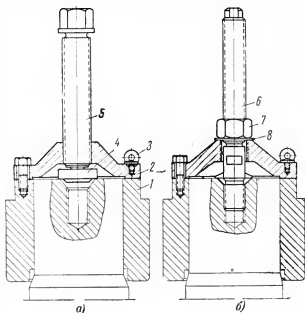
Приспособление для насадки и съема рычагов направляющих лопаток.
